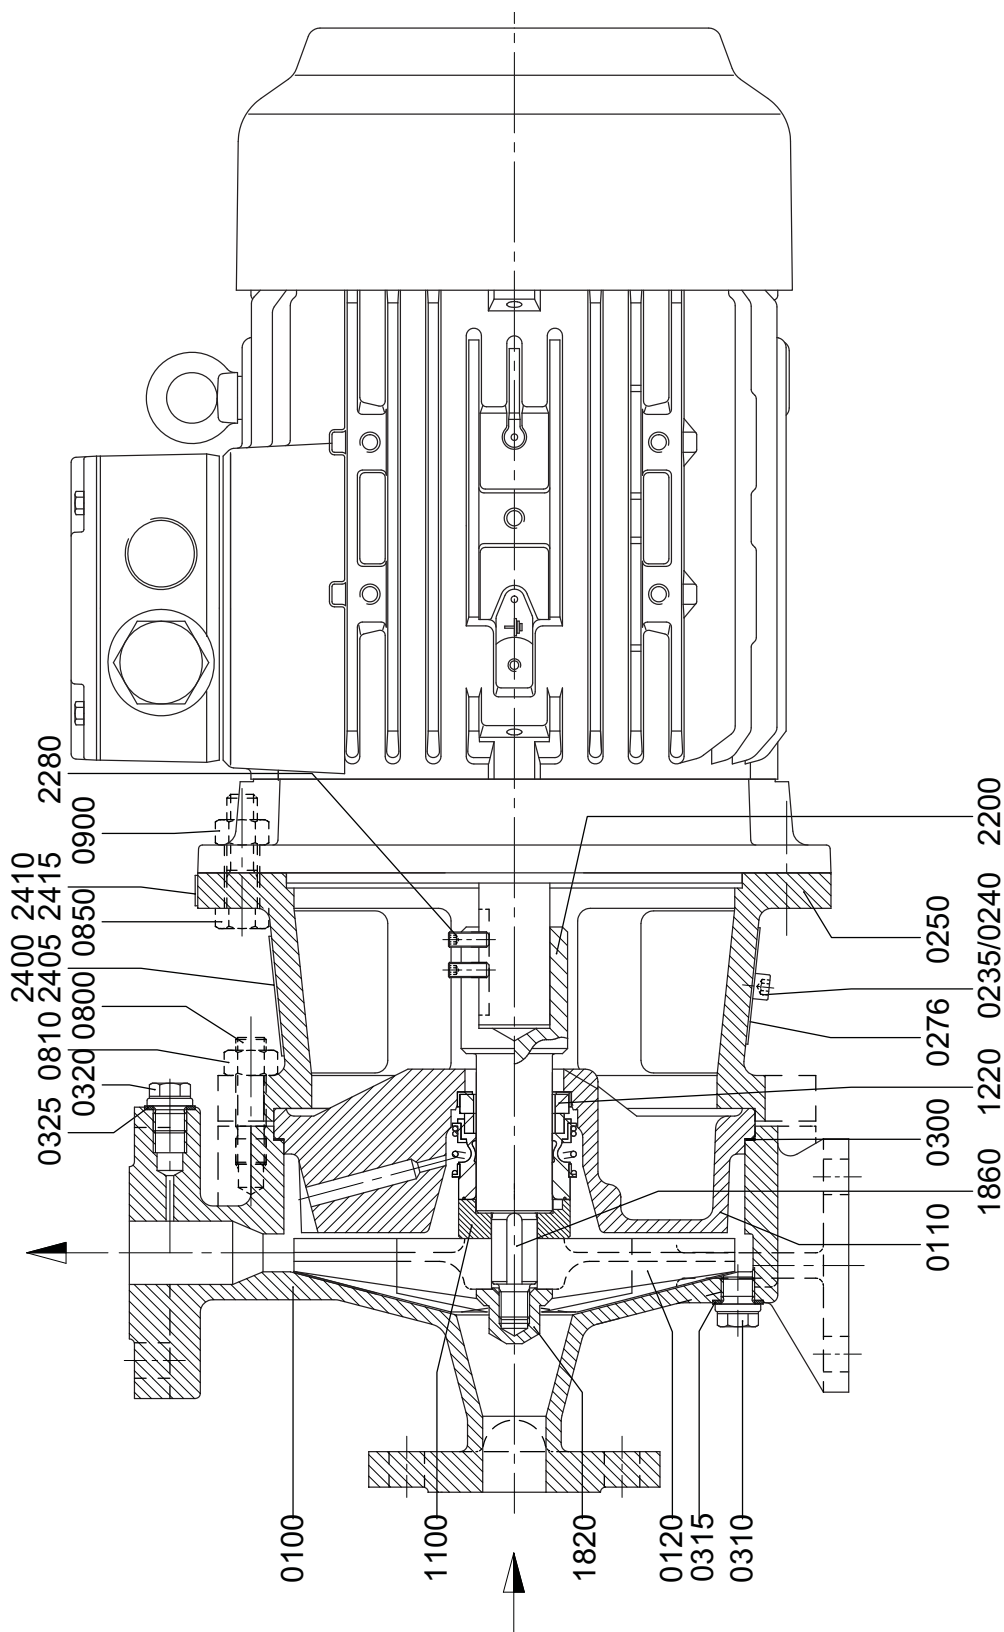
Чертеж в разрезе для 25-125, 25-160.
